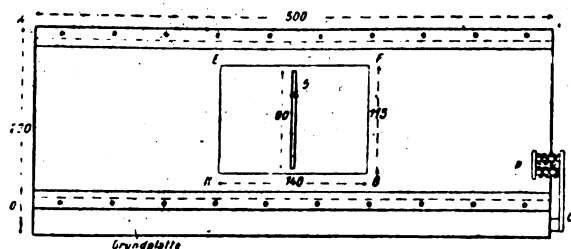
Dessin coté du cadre dans lequel coulisse le châssis.
